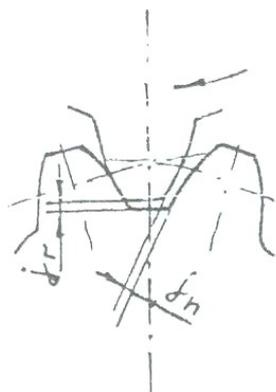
Схема образования радиального и бокового зазора в зубчатом зацеплении
